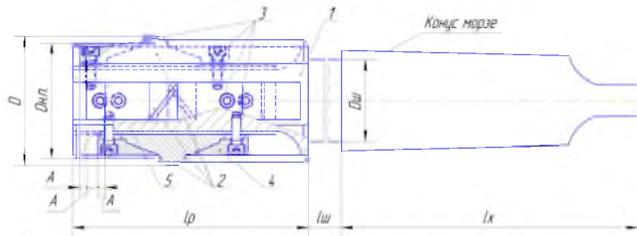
Общий вид резцовой сборной развёртки с безвершинными зубьями
